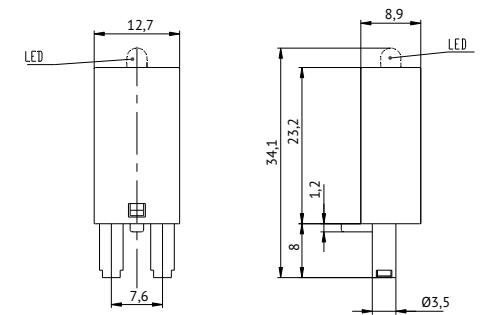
Габаритные, установочные присоединительные размеры фиксатора реле OptiRel 55-H5
